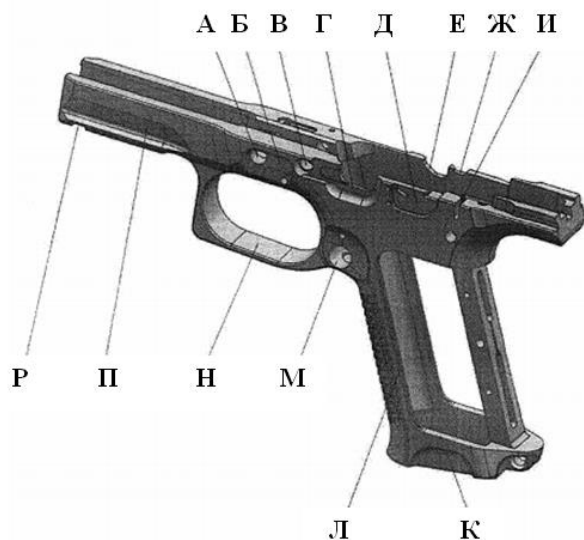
Вид рамки с левой стороны: А, В, М – отверстия; Б, Г, Д, Е, Ж, И, Л, Р – пазы; К – углубление; Н – предохранительная скоба; П – направляющая.
